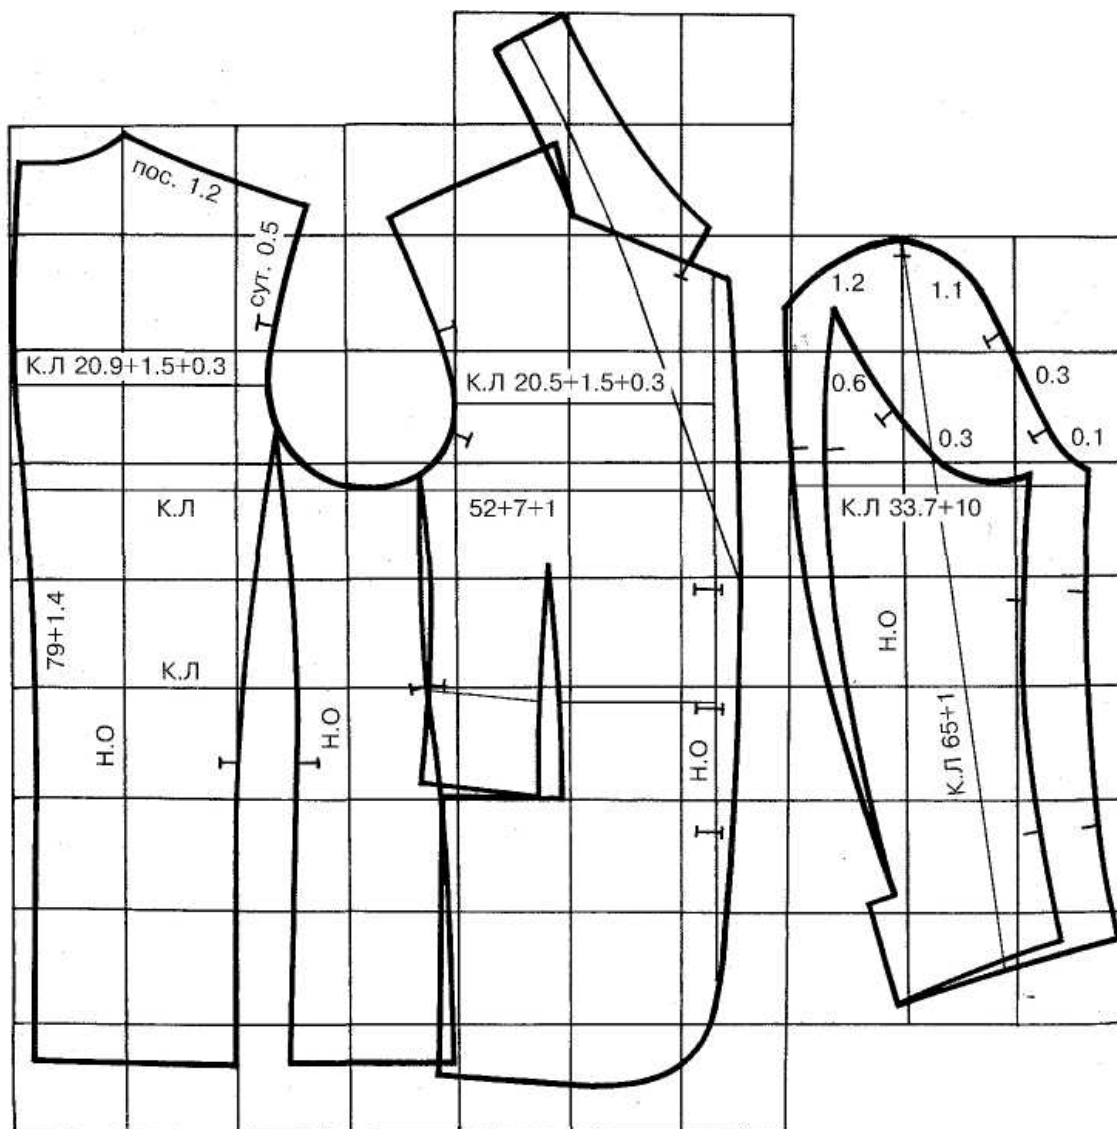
Технический чертеж конструкции пиджака 176-104-92
